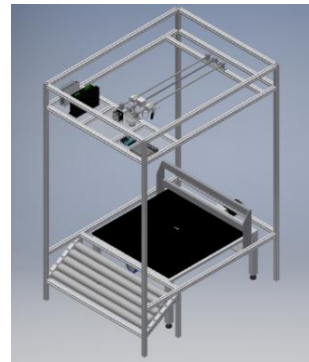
Prototipe Automatic Machine Measuring Of Mass And Dimension
